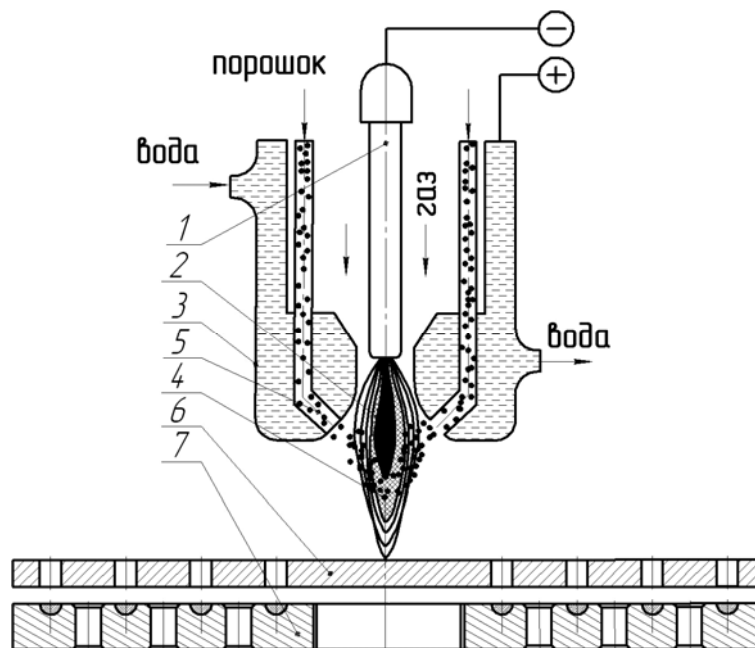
Схема плазмового напилення м'ясоподрібнювальної решітки: 1 – електрод; 2 – електрична дуга; 3 – сопло; 4 – плазмовий струмінь; 5 – транспортер бронзи; 6 – екран; 7 – решітка
